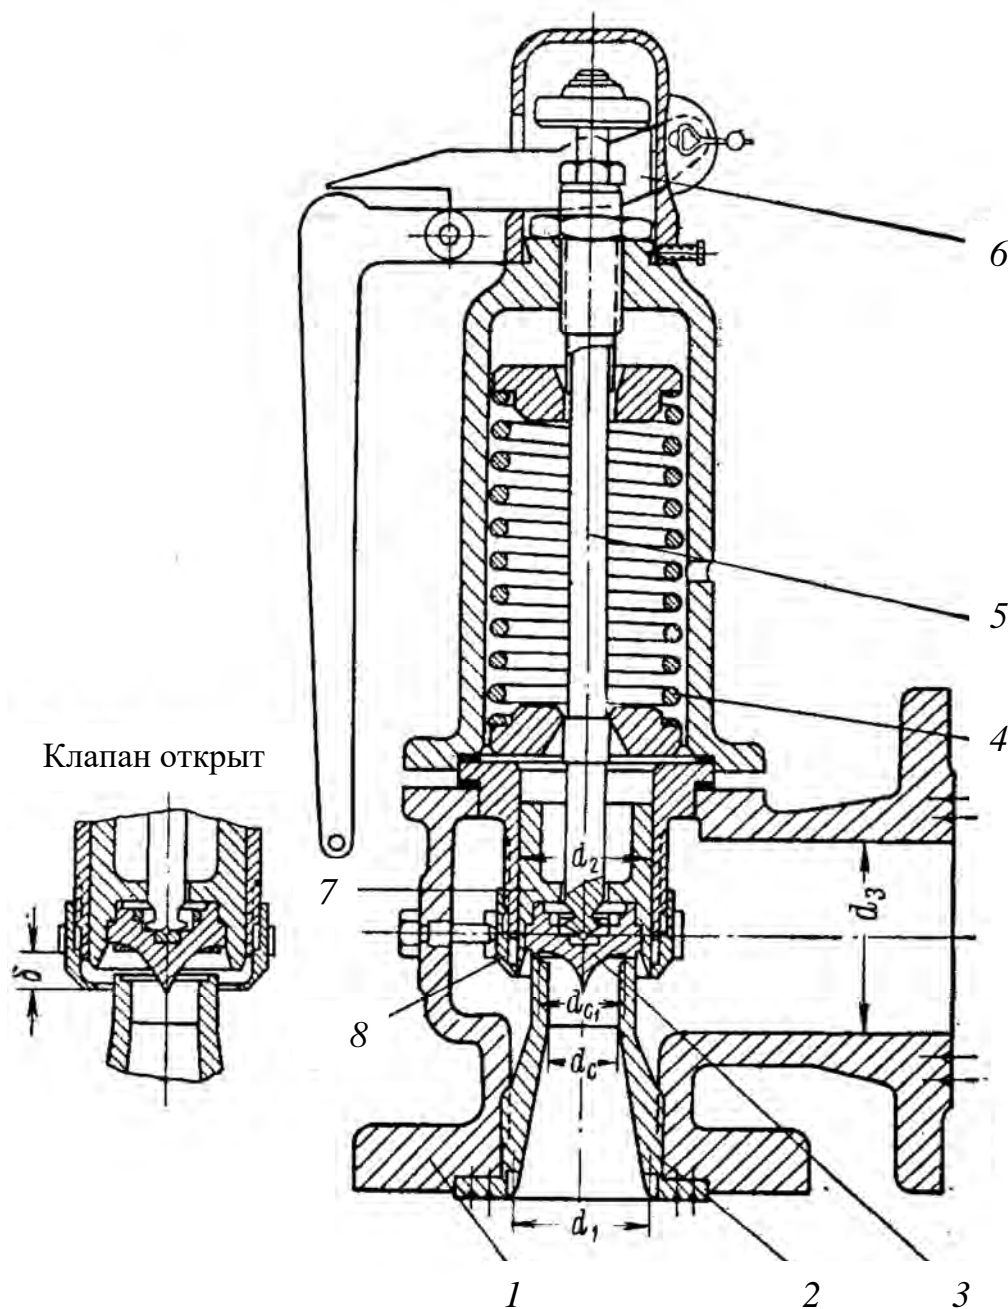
Пружинный предохранительный клапан: 1 – корпус клапана; 2 – седло; 3 – тарелка (запорный орган); 4 – пружина; 5 – шпindelь; 6 – рычаг; 7 – подвижная втулка; 8 – регулировочная гайка
